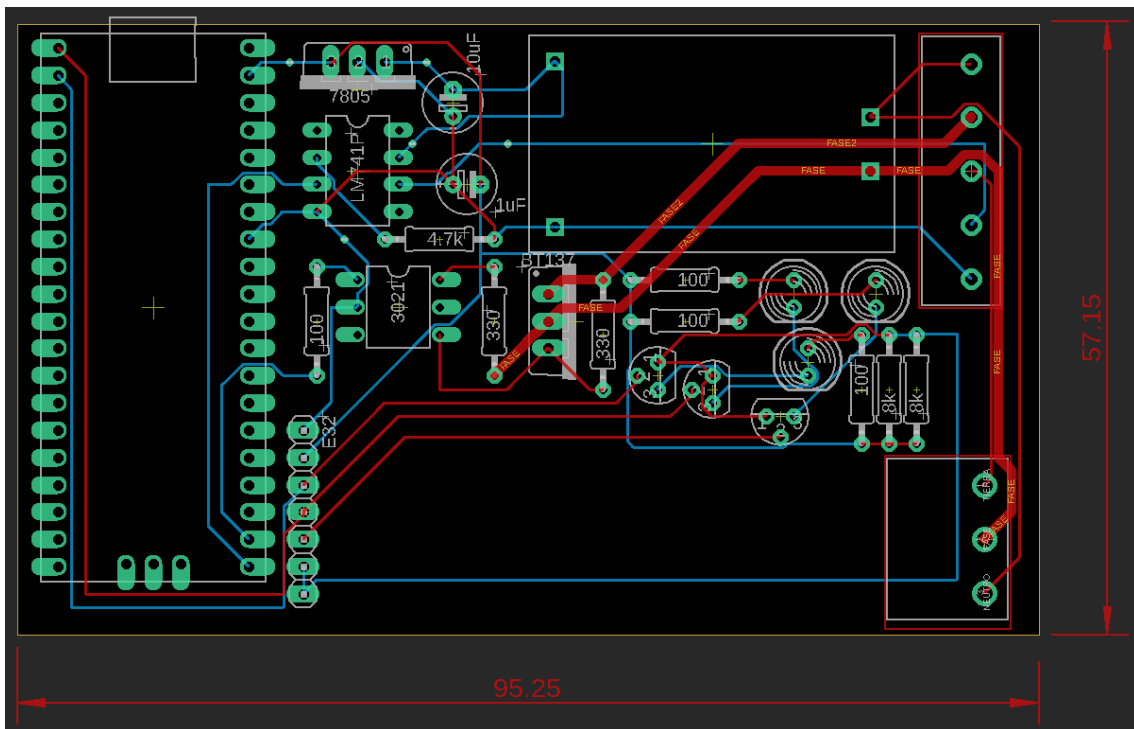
Diseño de la placa pcb del circuito integrado en la luminaria.
